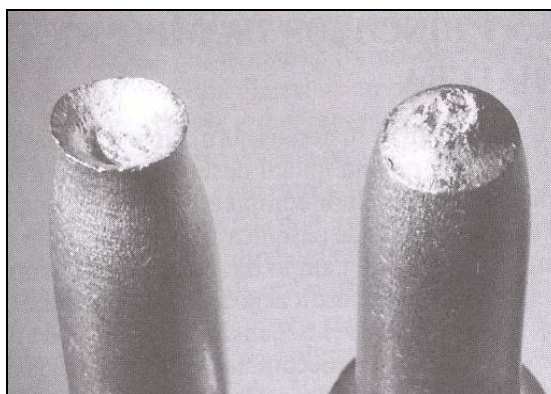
Superfície de fractura de um material dúctil (Callister Jr., 2002).
